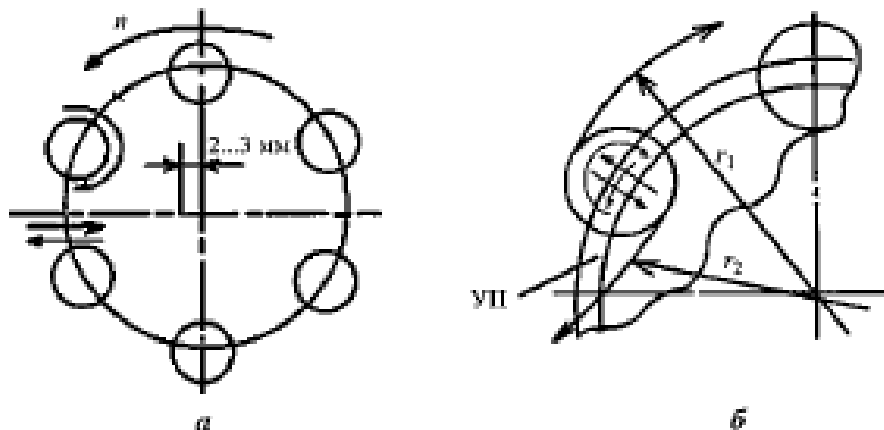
Кинематика процесса микрорезания (n – главное направление вращения, r_1 и r_2 – радиусы траекторий рабочих дисков: а – схема расположения рабочих дисков; б – кинематическое движение рабочего диска)
